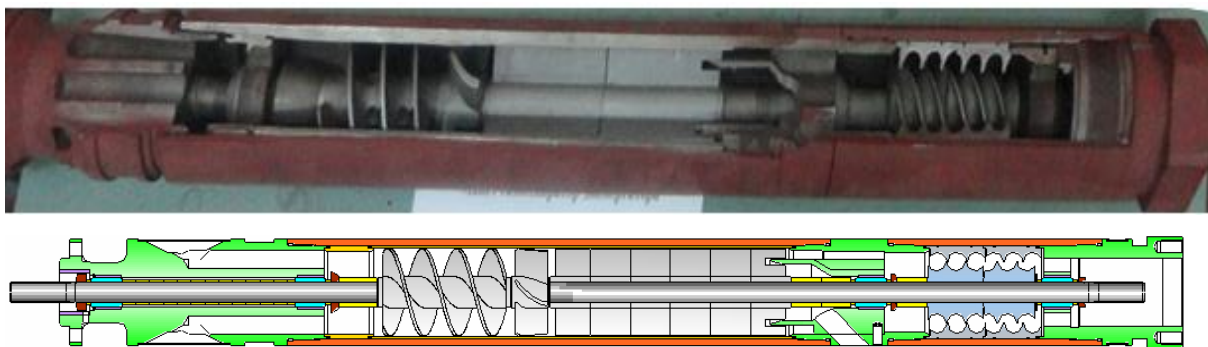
Чертеж и разрез газосепаратора-диспергатора ГДН 5
